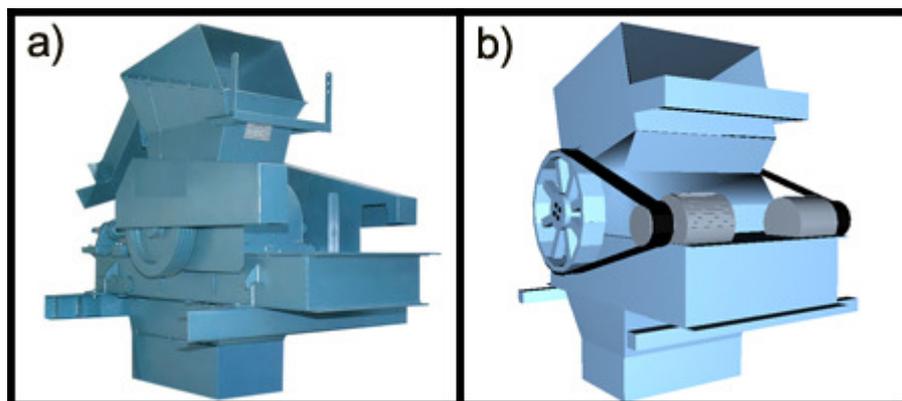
Desintegradora: a) Foto Real e b) Modelagem.
